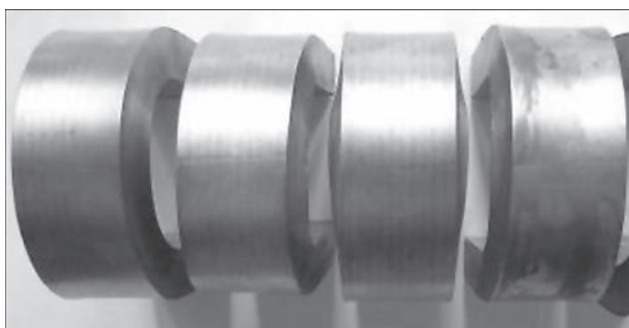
Образцы сварного соединения, испытанные на статический изгиб после термообработки
